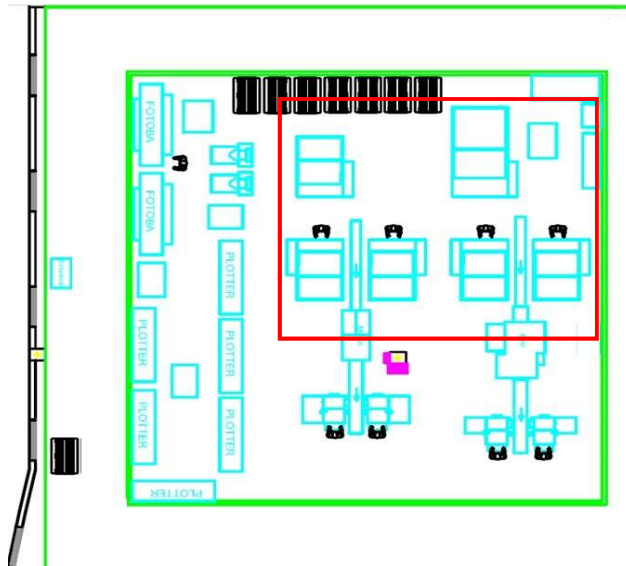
Vista en planta de la zona donde se detectó la incidencia nº6 : Fast Frame. Fuente: Elaboración propia.
